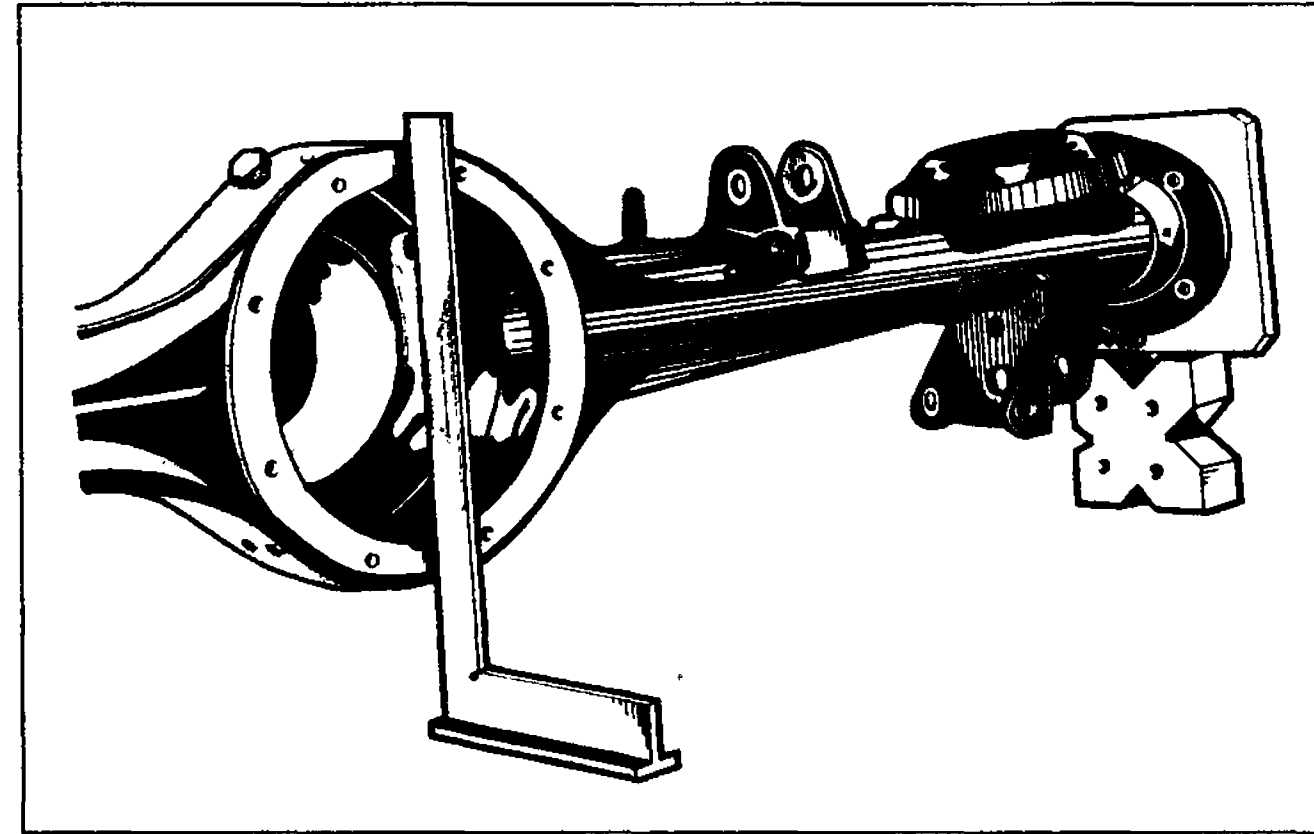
Проверка перпендикулярности поверхности крепления редуктора
